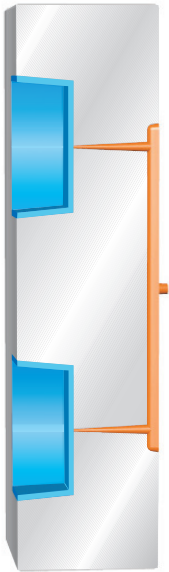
Dreiplatten-Kaltkanalwerkzeug mit sekundärem Angusskegel, der die Kavitäten mit Schmelze versorgt
